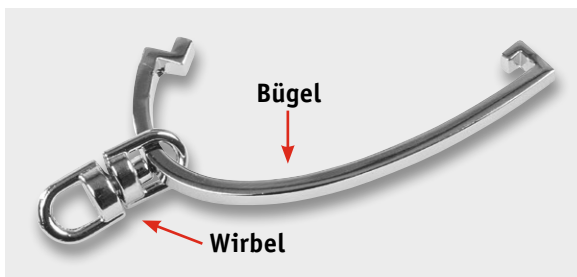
Zu Beginn der Montage ist der Metallbügel wie hier gezeigt in den Wirbel für die Schlüsselbundbefestigung einzuführen.
